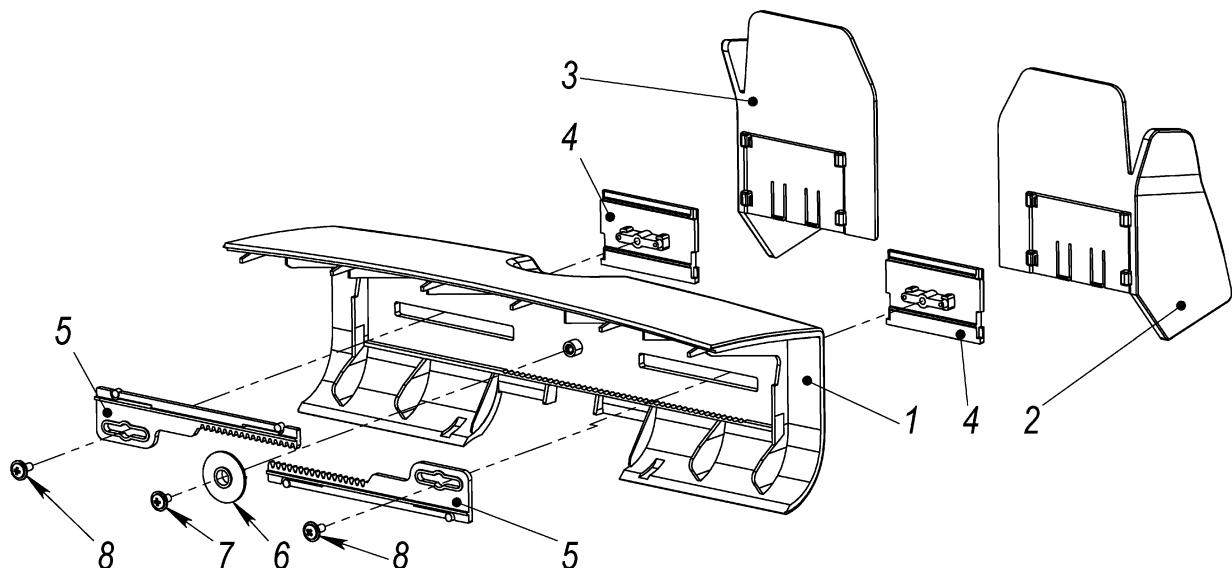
Узел крышки верхней в сборе EBKM.00D800.02.13.000
